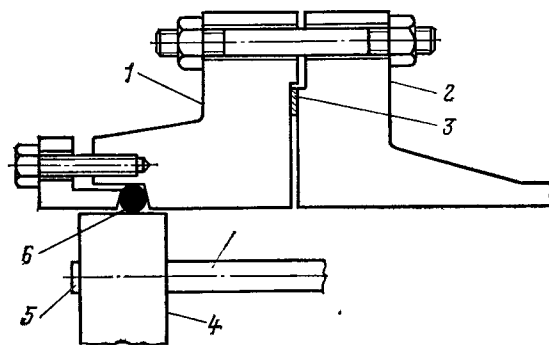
Фланец и сальник для испытания теплообменника с плавающей головкой:
